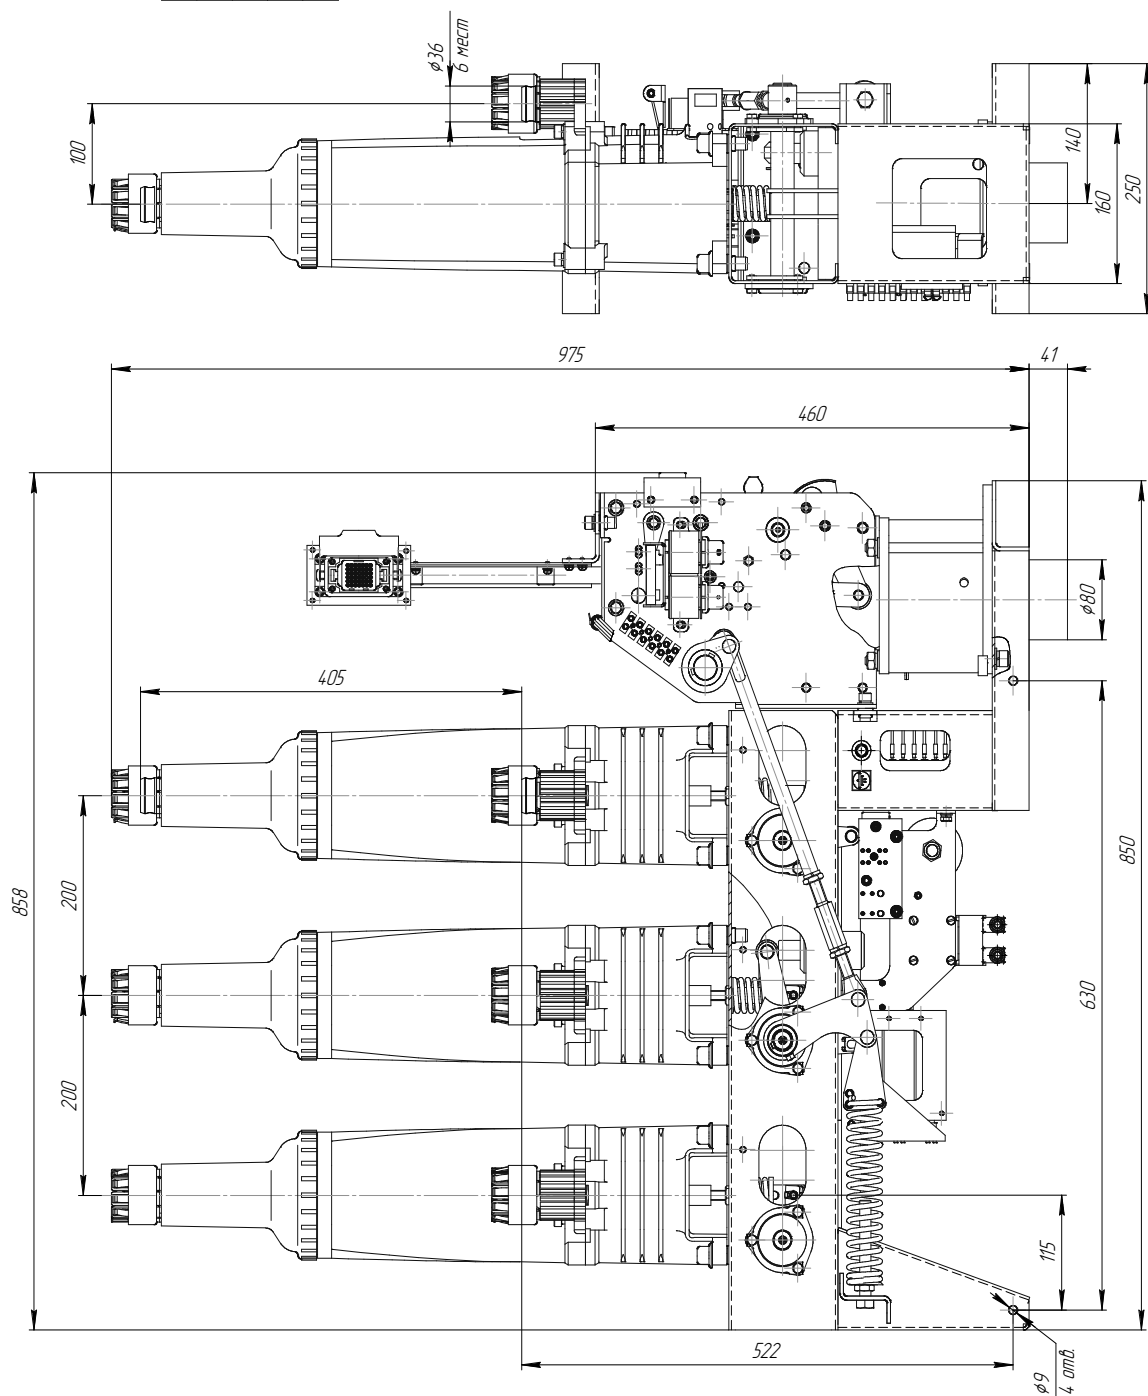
Габаритные, присоединительные и установочные размеры выключателя типа ВВУ-СЭЩ-Э4-10-20/1000(1600)
